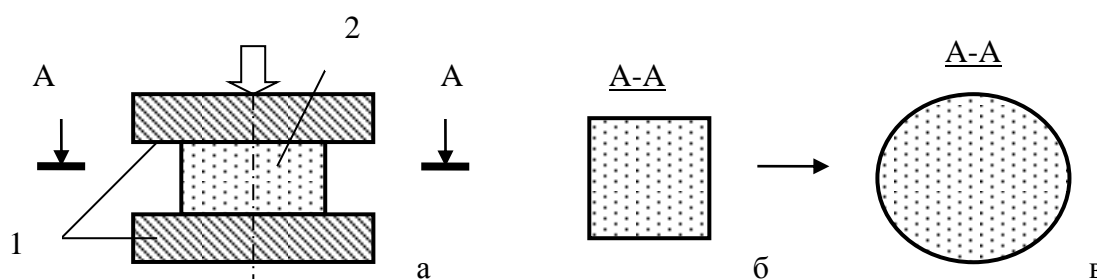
Схема преобразования квадратной в плане заготовки в круглую: 1 – бойки, 2 – заготовка; а – схема осадки, б – вид в плане исходной заготовки, в – вид в плане осаженой заготовки
